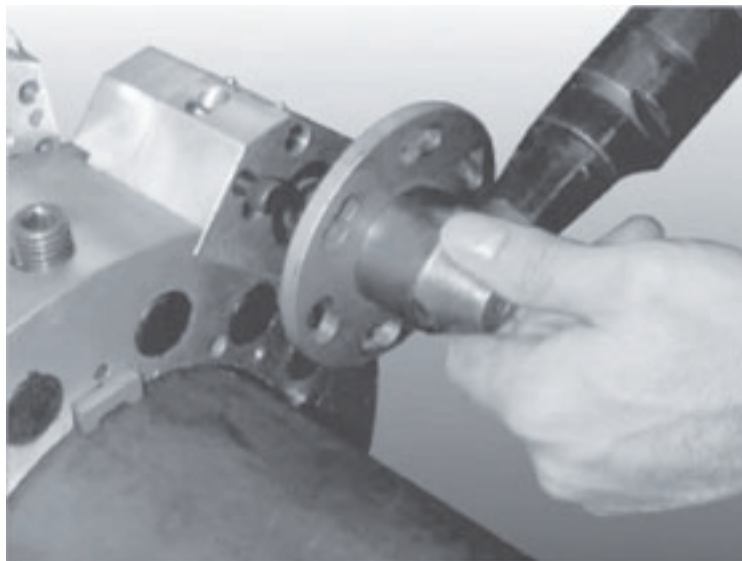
Выровняйте болтовые отверстия фланца двигателя по винтам с головкой с углублением под шестигранник в корпусе ведущей шестерни.
